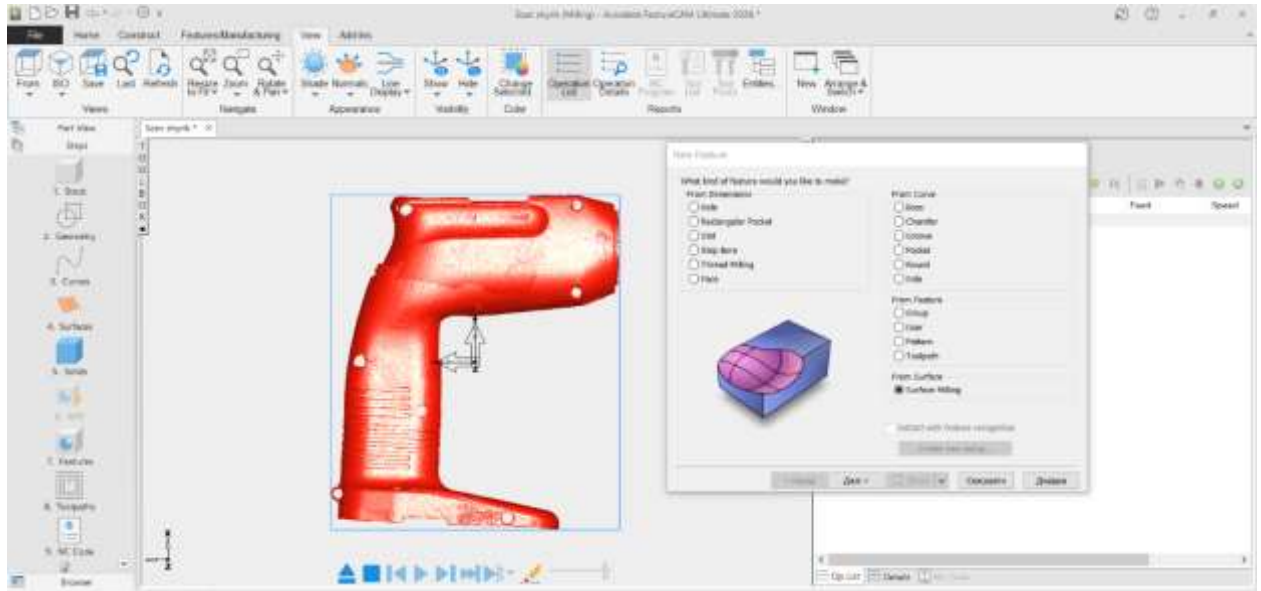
Обрання режиму фрезерування як криволінійна поверхня
